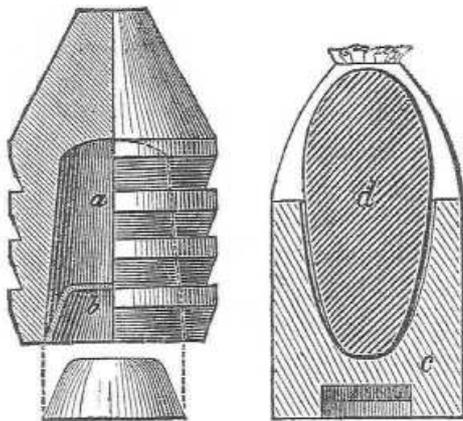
Miniégeschoss und Dreyse-Langbleigeschoss,
